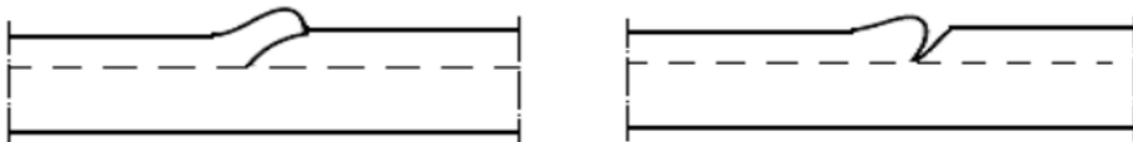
Эскиз дефекта сварного шва
